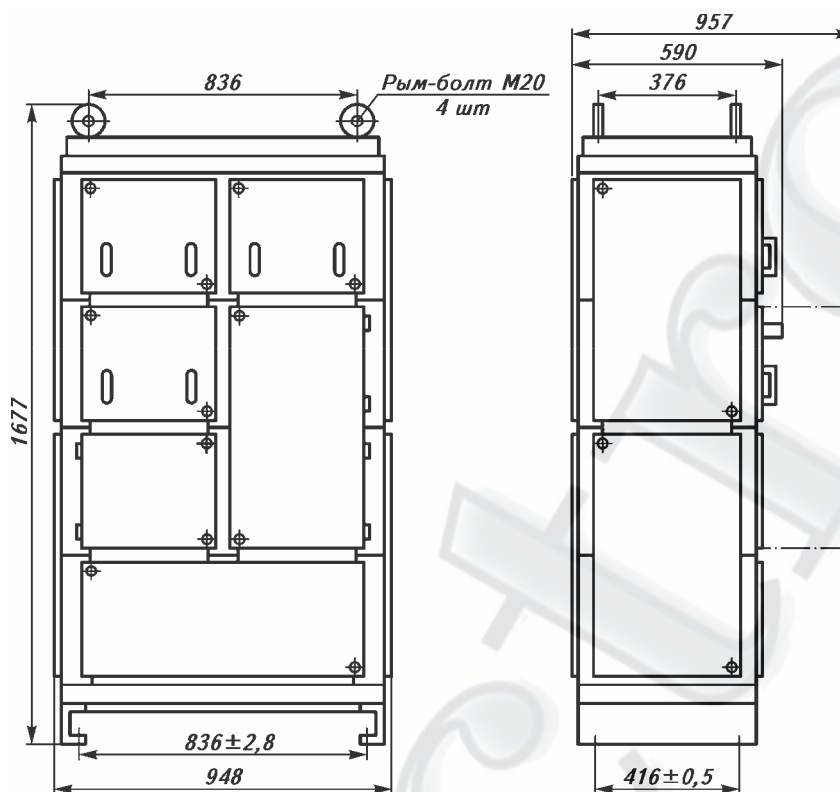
Общий вид, габаритные и установочные размеры шкафа управления агрегатом АГПМ-7,5
